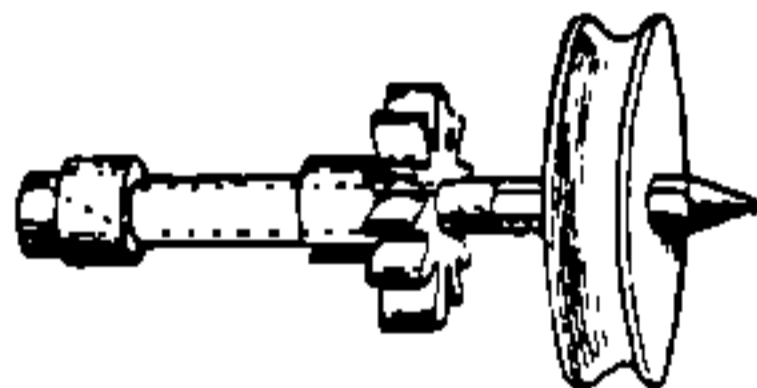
Rocchetto calzante montato su un albero ruotante, non sporgente da esso.
